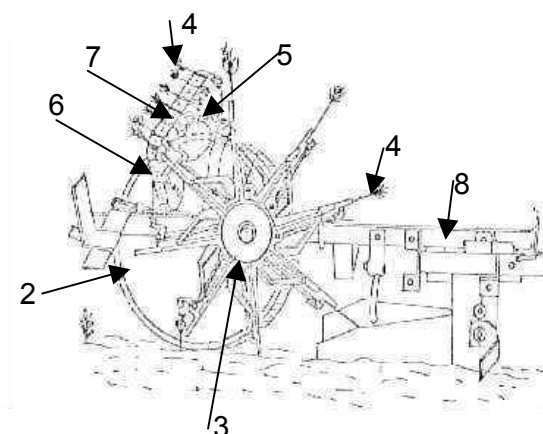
Concepção utilizando braços transplantadores (Patente 886146)
